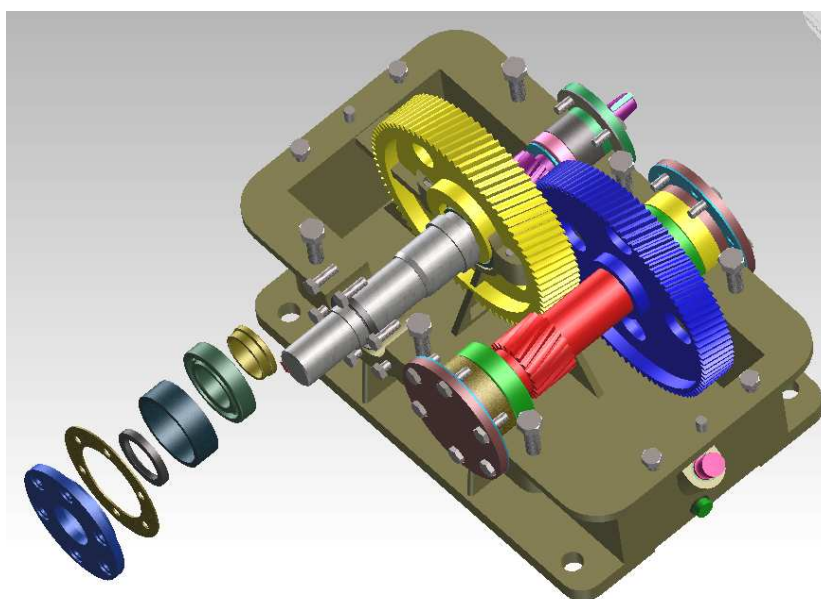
Трехмерная модель редукторной передачи с демонстрацией устройства узла тихоходного вала
